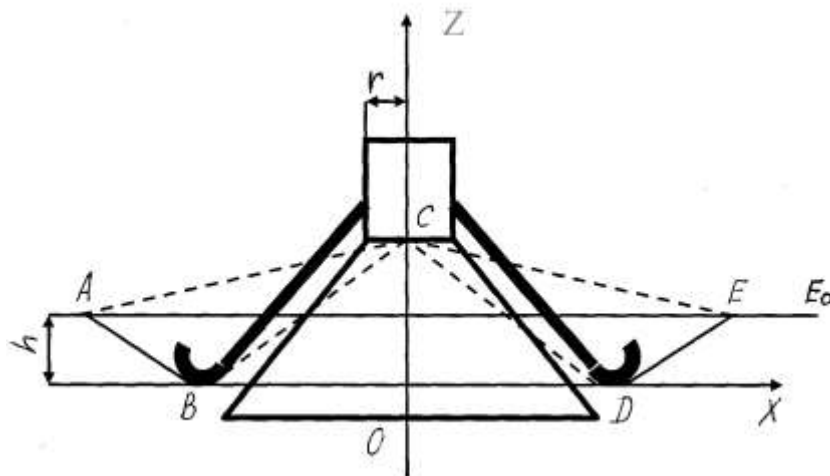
а. Розрахункова схема конусного пристрою для натягу нитки
